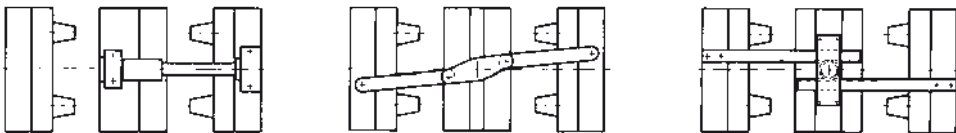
Mögliche Antriebsarten des Werkzeugmittelsegmentes bei Etagenwerkzeugen [13.12]
